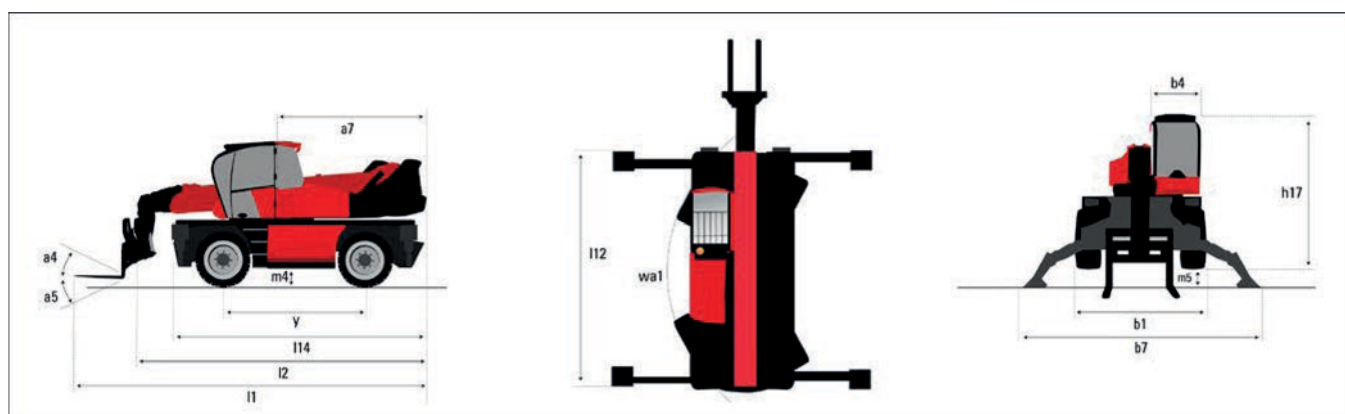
Dimensioni (vista laterale, frontale e dall'alto)
